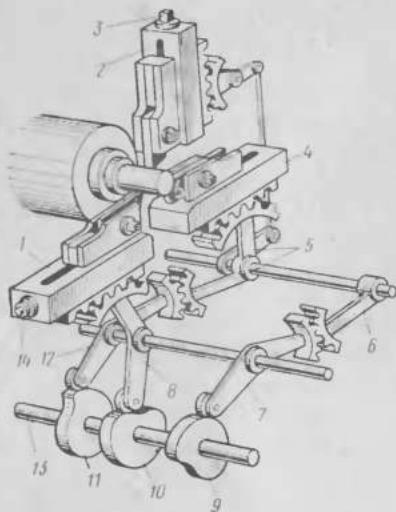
Схема расположения поперечных суппортов токарно-револьверного автомата
